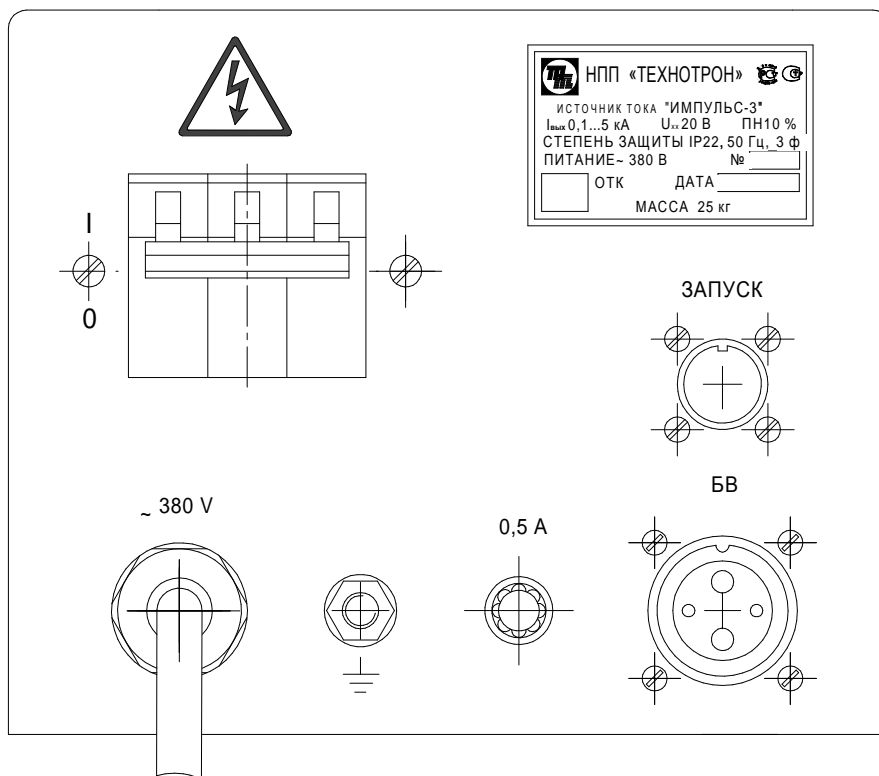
Панели источника тока контактной сварки "Импульс-3"
